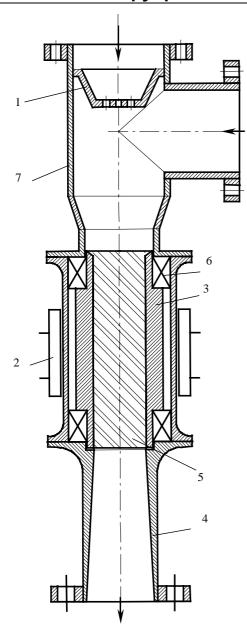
Струйный насос с вращающейся камерой смешения: 1 — сопло; 2 — привод; 3 — камера смешения; 4 — диффузор; 5 — направляющий аппарат; 6 — подшипник; 7 — камера приемная
